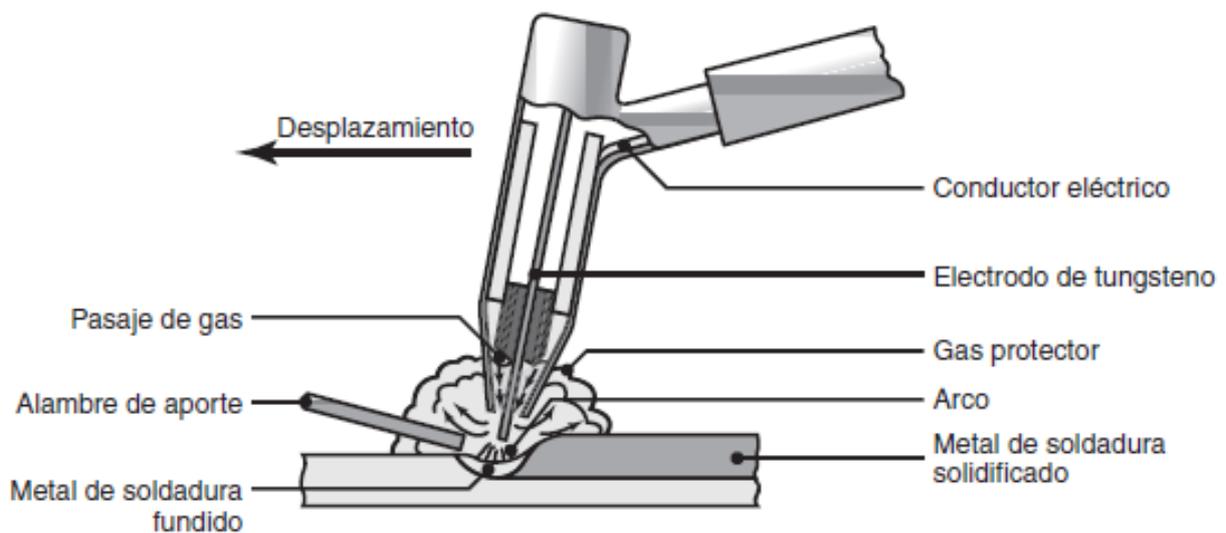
Proceso de soldadura por arco de tungsteno y gas (Fuente: Manufactura, Ingeniería y Tecnología)
